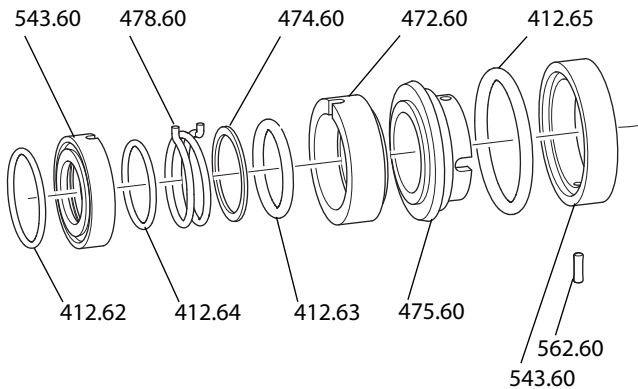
Caso d'applicazione B, terminare il montaggio sull'albero (III)
